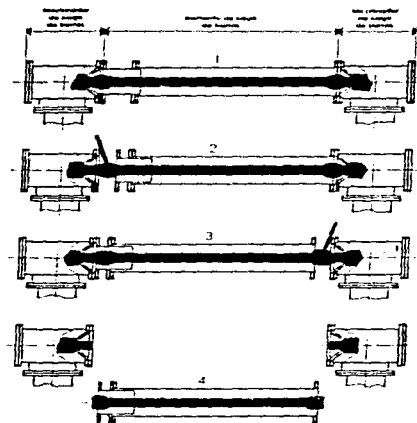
EXTRACCION DE UN ELEMENTO DE JUEGO DE BARRAS
